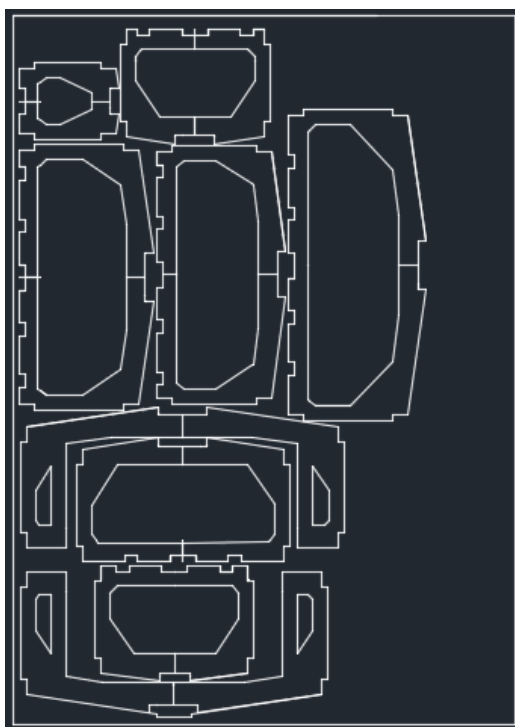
Vista composición cuadernas sobre plancha formato 2D (Fuente: Propia Autocad)
